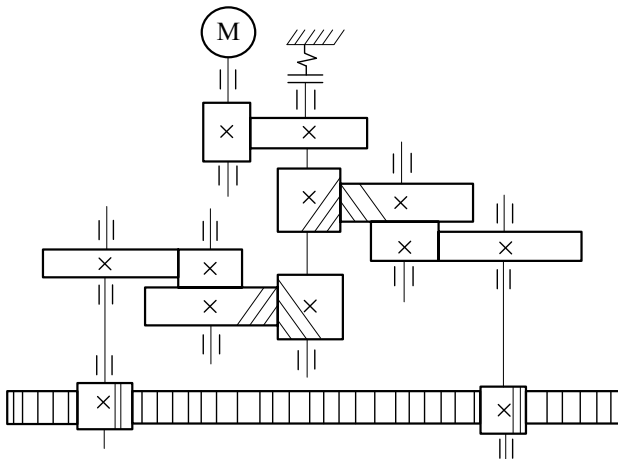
Привод с выбором зазора в конечной кинематической цепи
